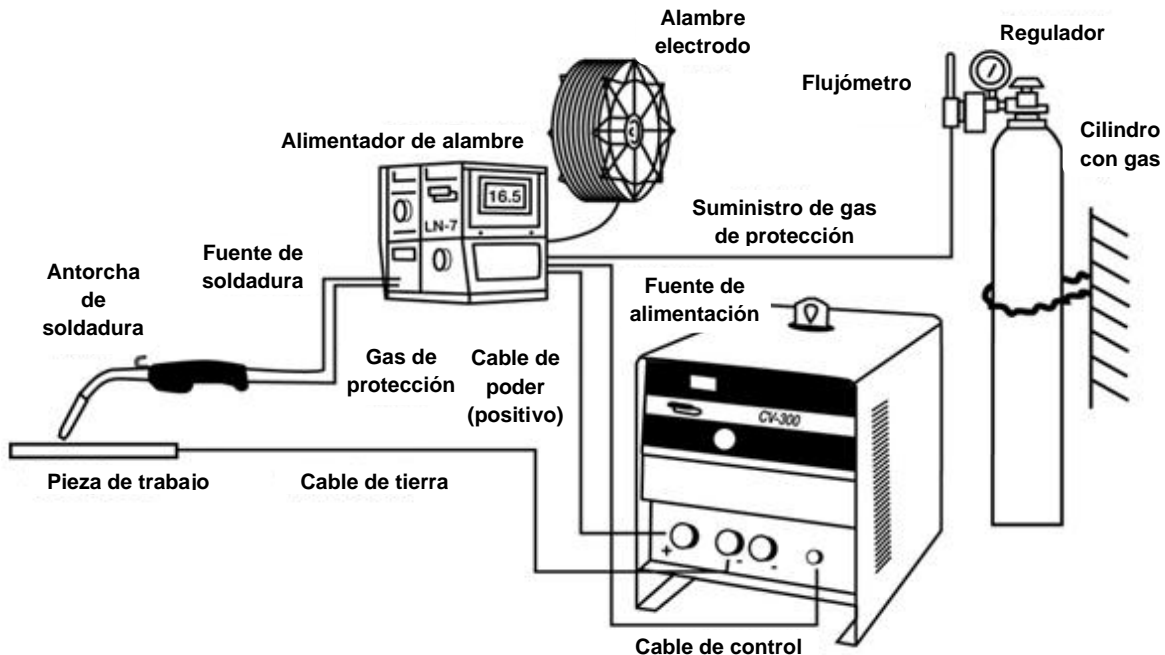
Componentes de un sistema completo de soldadura GMAW (2).
